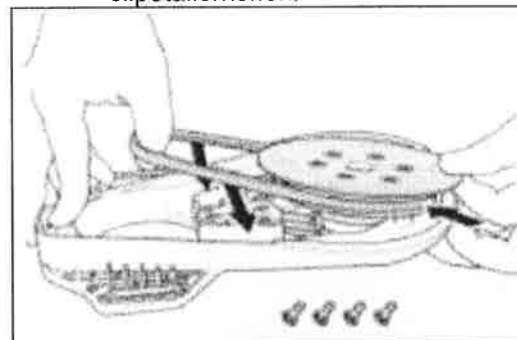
Sett opplagringen til slipetallerkenen med kilereim inn i forsatsen. Pass på at hullene stemmer overens.
